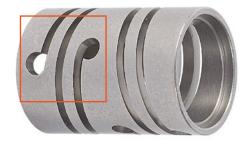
Machined Spring mit Stressentlastungsbohrungen
